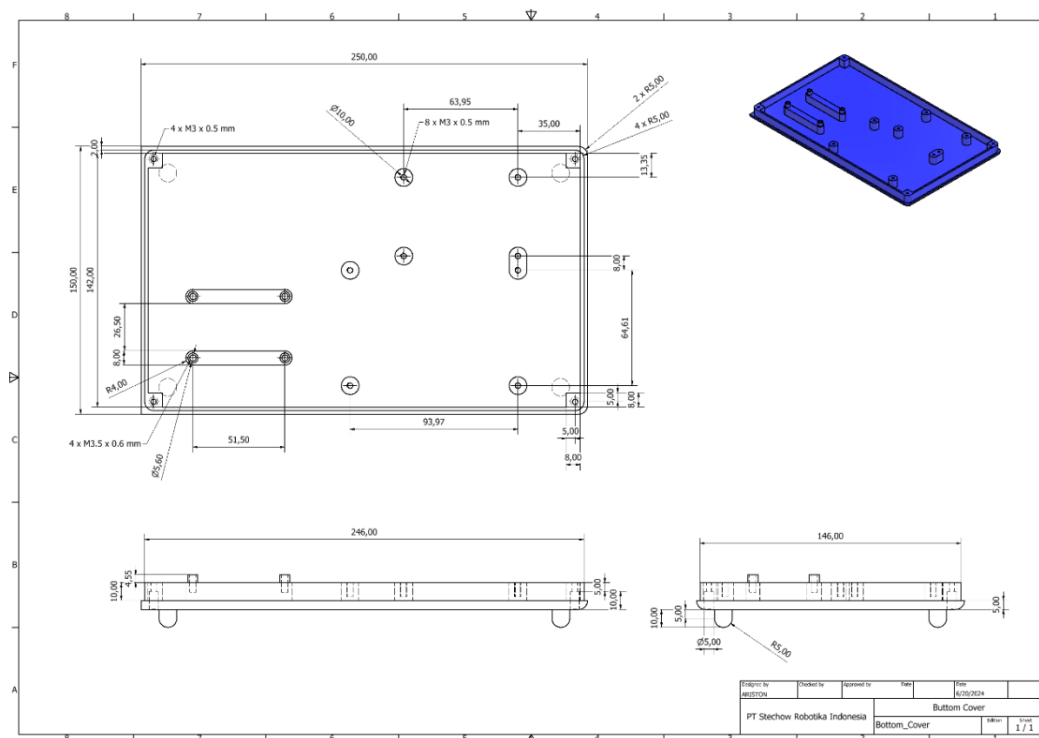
15 Tampak Bawah Cover Utama Drawing
